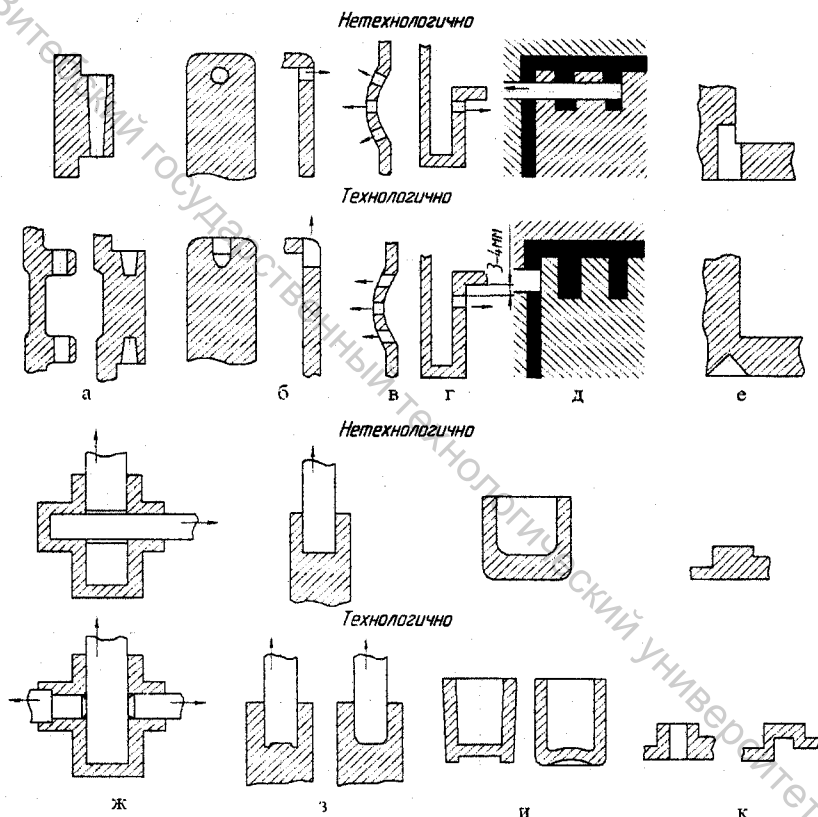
Конструкционные варианты оформления отверстий в отливках
